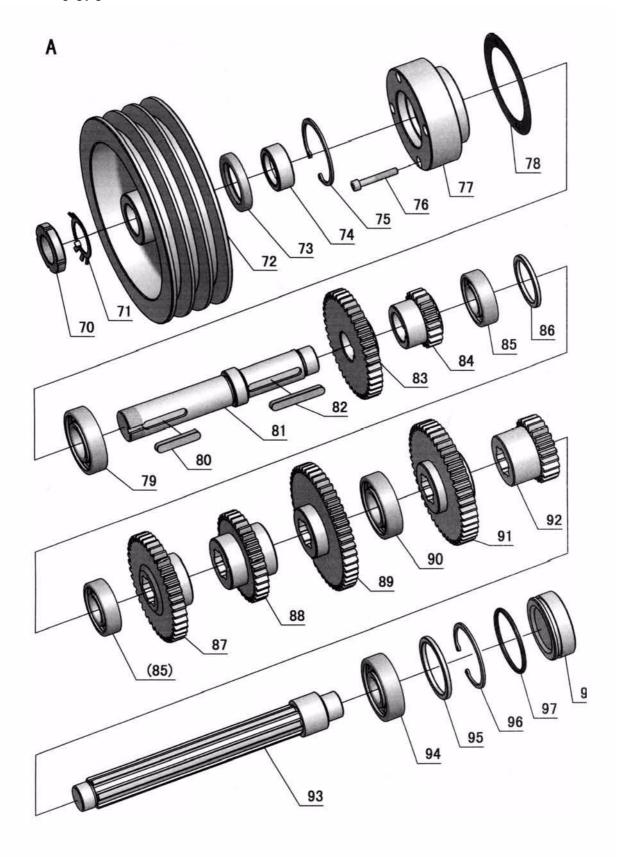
Spindelstock 3 von 8 - Headstock 3 of 8
